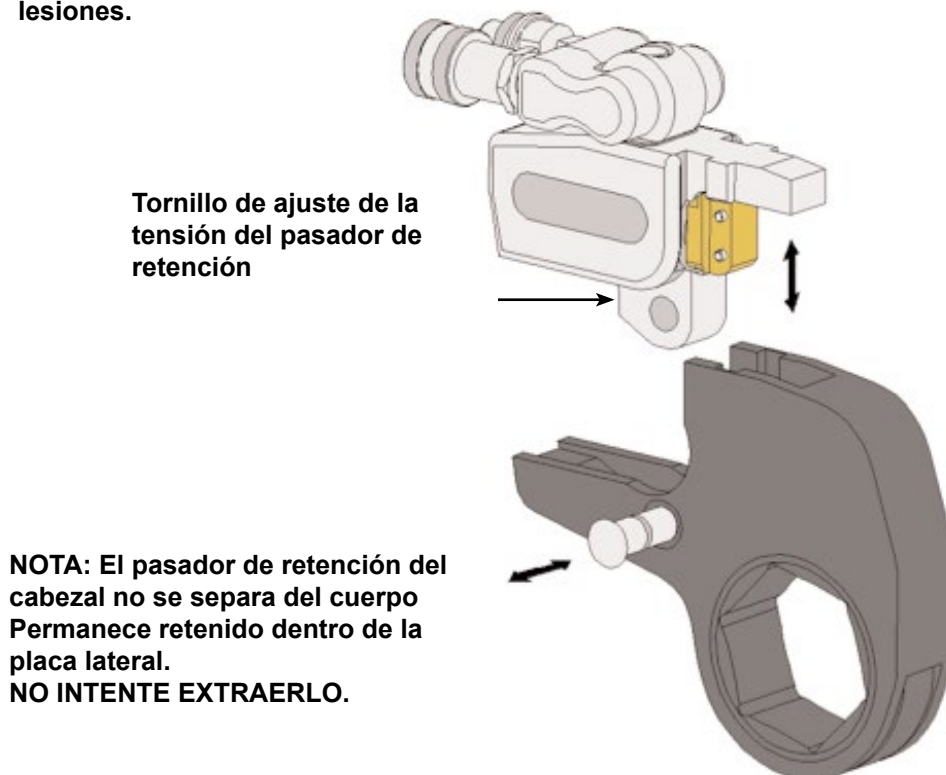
Montaje y desmontaje del cuerpo y del cabezal actuador
